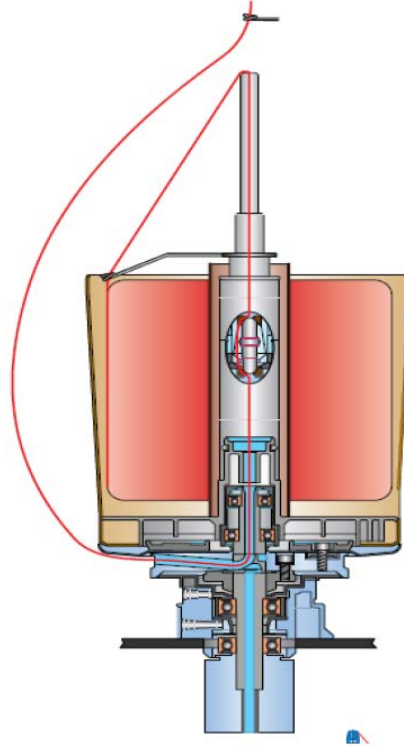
Ring büküm makinesi (Milli Eğitim Bakanlığı, 2011)
